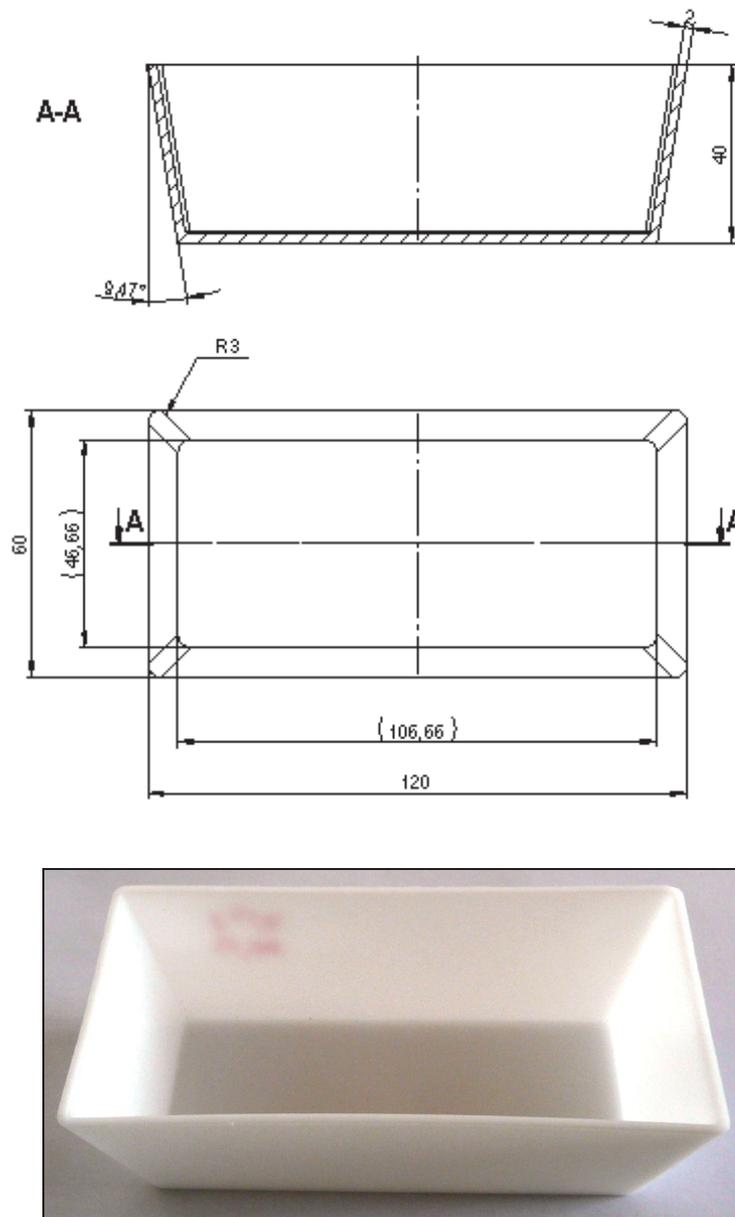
Geometrie und Abbildung des Prüfkästchens (die Maße beziehen sich auf die Werkzeugkavität).
